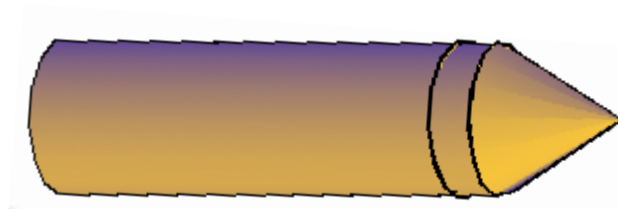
Vista 3D del cilindro espumado generado con el dado de extrusión y la cámara de expansión.
